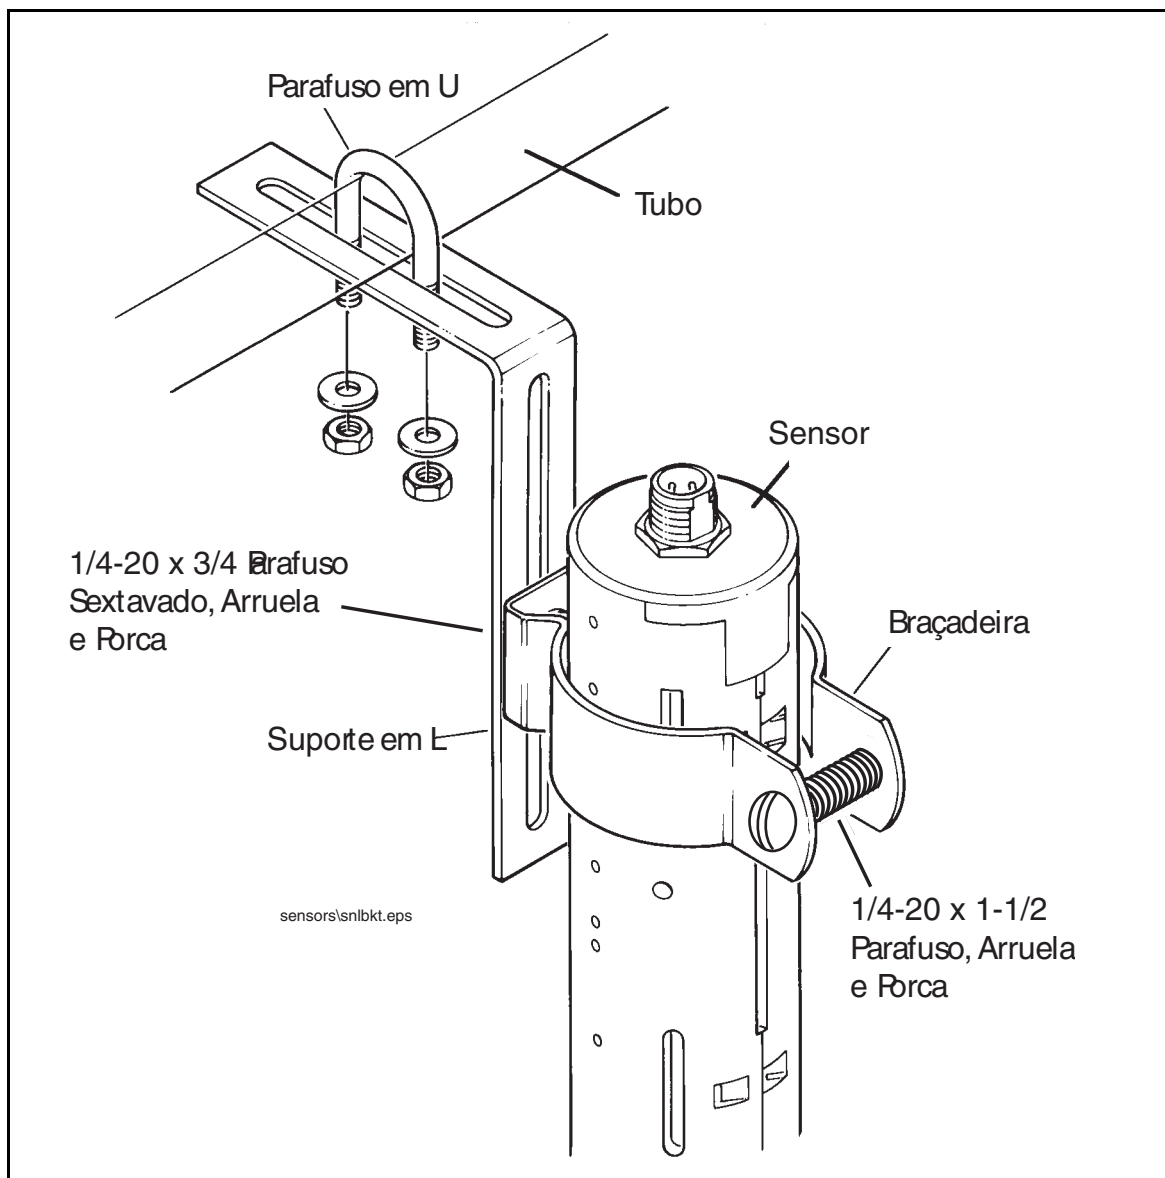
Montagem do Kit em um Suporte rígido com braçadeira
